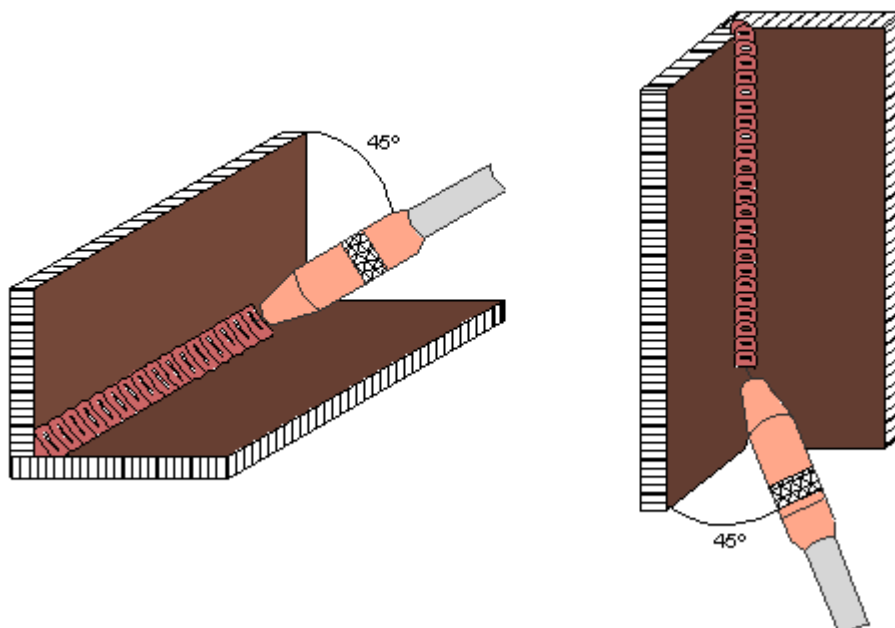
Soldadura en ángulo interior posición horizontal y vertical
